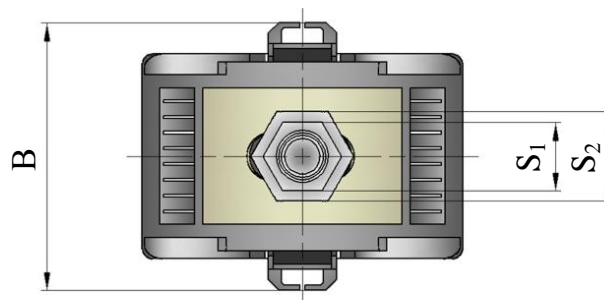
Габаритные и присоединительные размеры зажима ЗПО 1,5-10.
